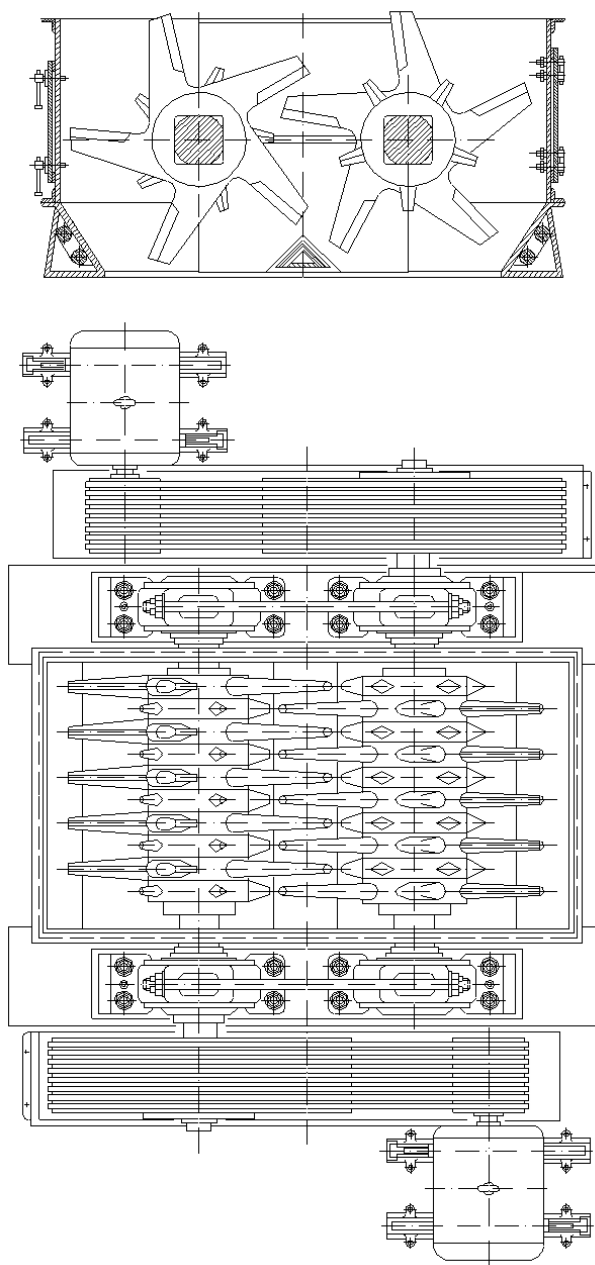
Двухроторна ножова дробарка СМД-153
